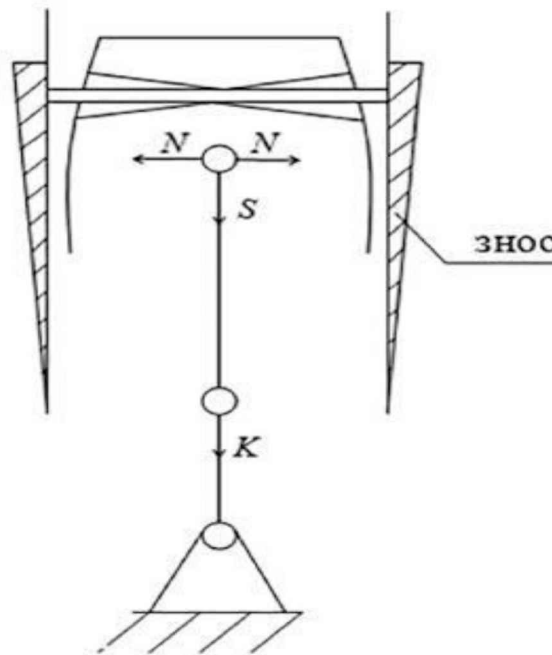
Положення максимального зношування деталей циліндропоршневої групи
